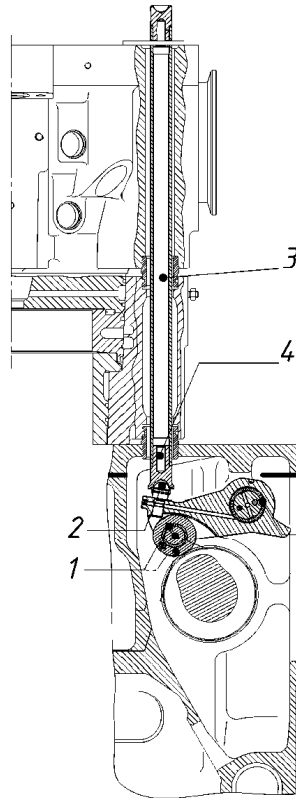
Механізм приводу клапанів: 1 – ролик штовхача; 2 – ударник; 3 – штанга штовхача; 4 – наконечник штанги
